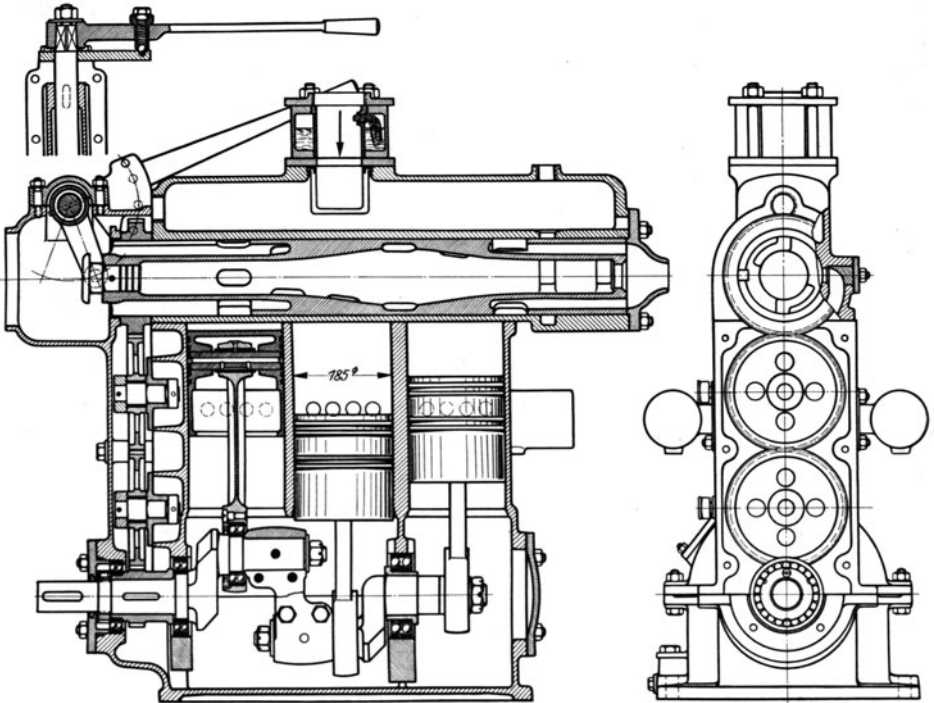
Umsteuerbarer Blockmotor der Frankfurter Maschinenbau-A. G. (50 PS).
